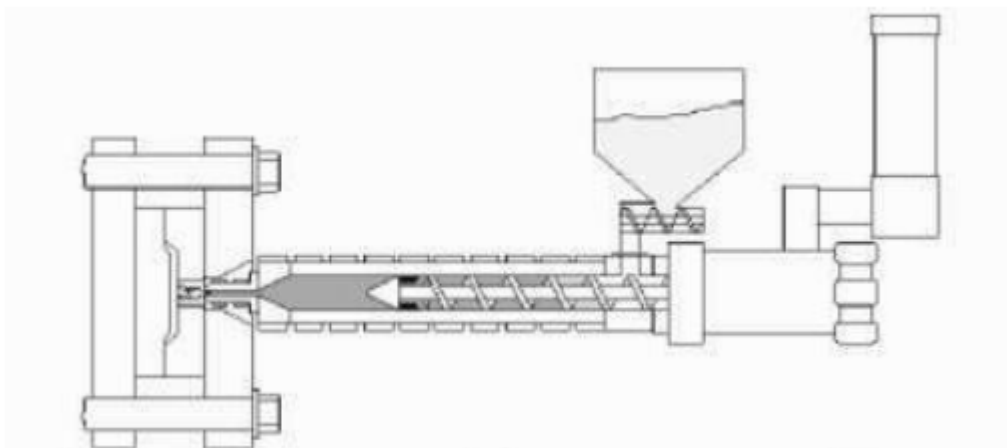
Processo de fundição por tixomoldagem. (Adaptado de Kainer,2003).
